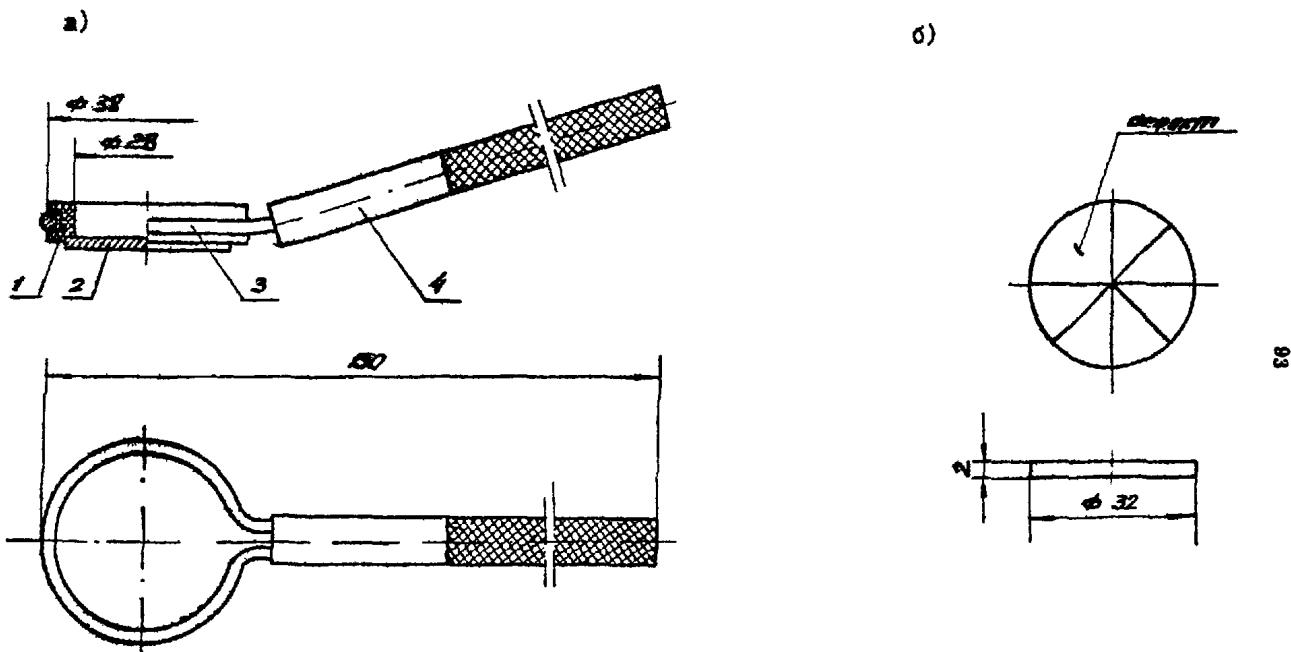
Рис. I. Устройство для определения направления намагничивающего поля и чувствительности контроля: а - устройство в сборе; б - образец.'
